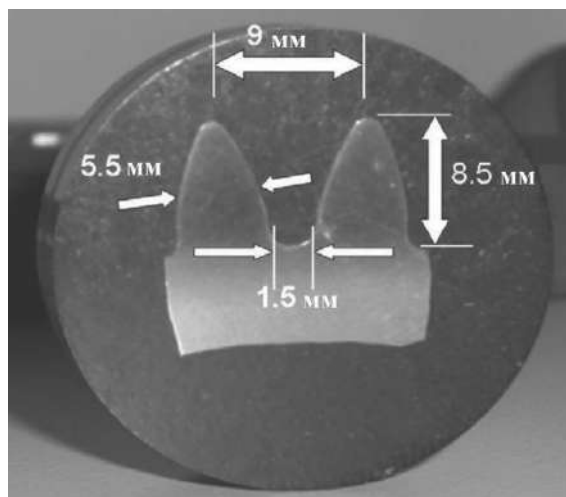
Геометрические размеры шестерни для ИА с ПК [31]
